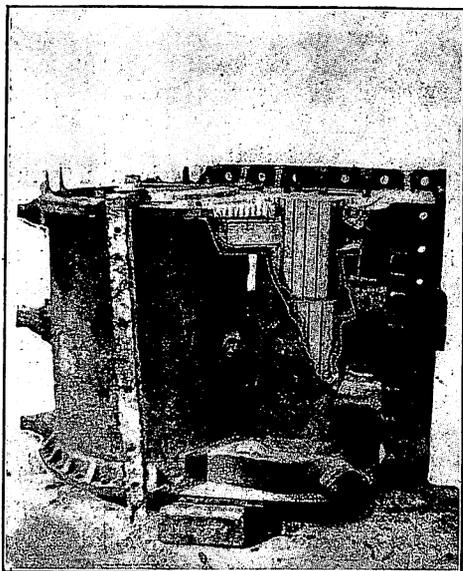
Beschädigter Lokomotivzylinder, eingefornt.
